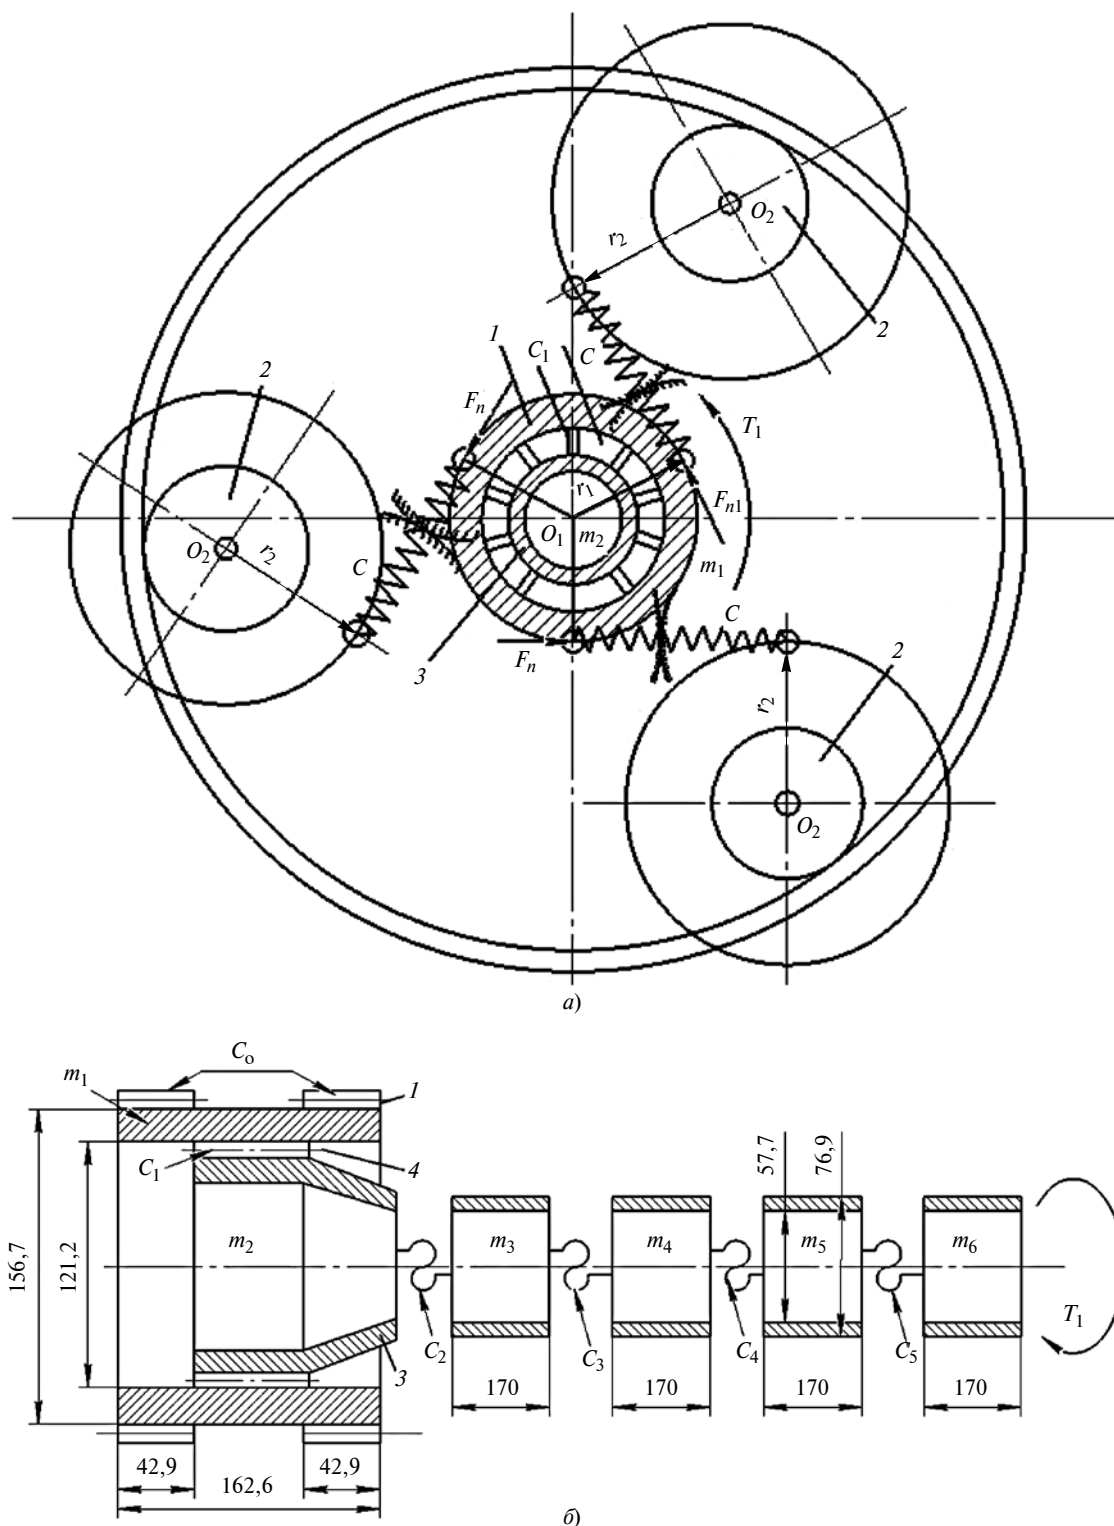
Схемы упругой модели редуктора (а) и разбивки приводного вала на пять участков (б)
